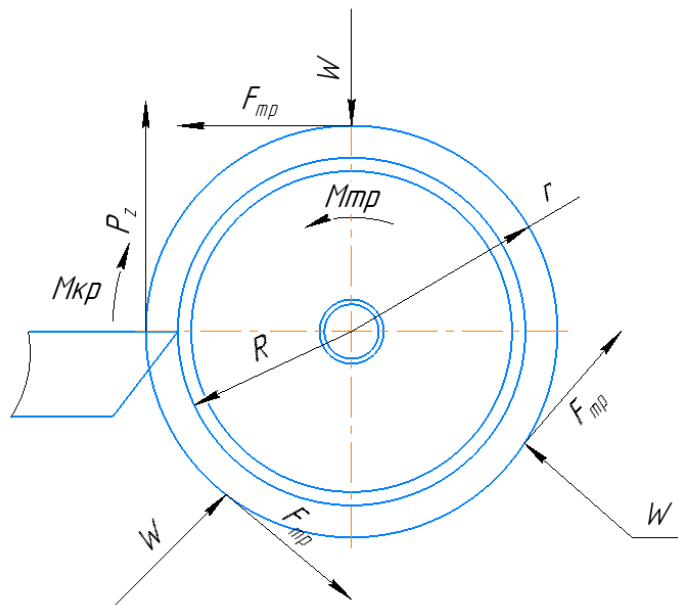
Схема розрахунку сили закріплення заготовки
